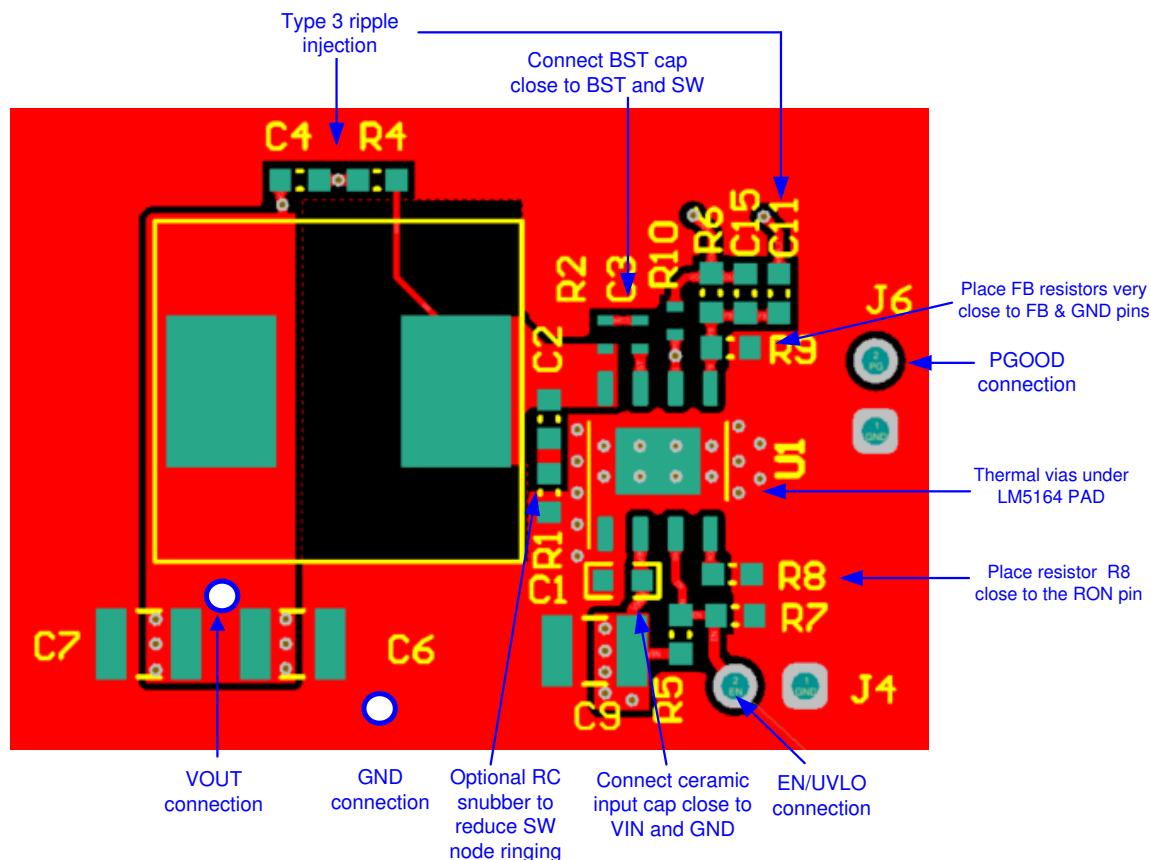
LM5164-Q1 片面 PCB レイアウトの例
